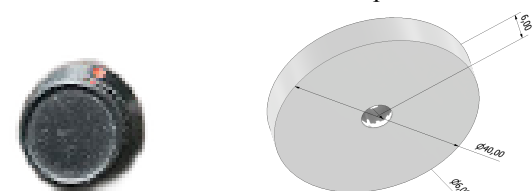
Perilla y dimensiones del disco en impresión 3D.
